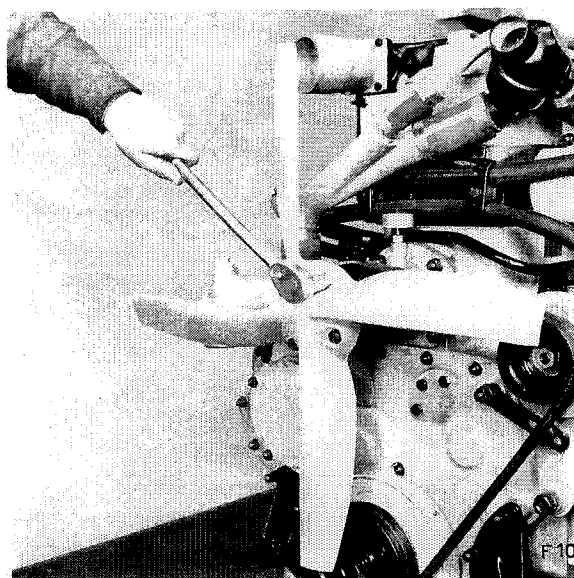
Lösen der Befestigungsschrauben am Ventilator
